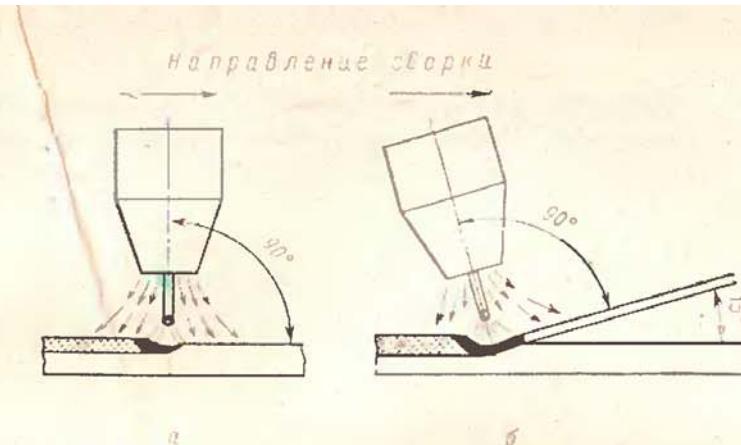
Расположение горелки при ручной аргоно-дуговой сварке исплавляющимся электродом:
